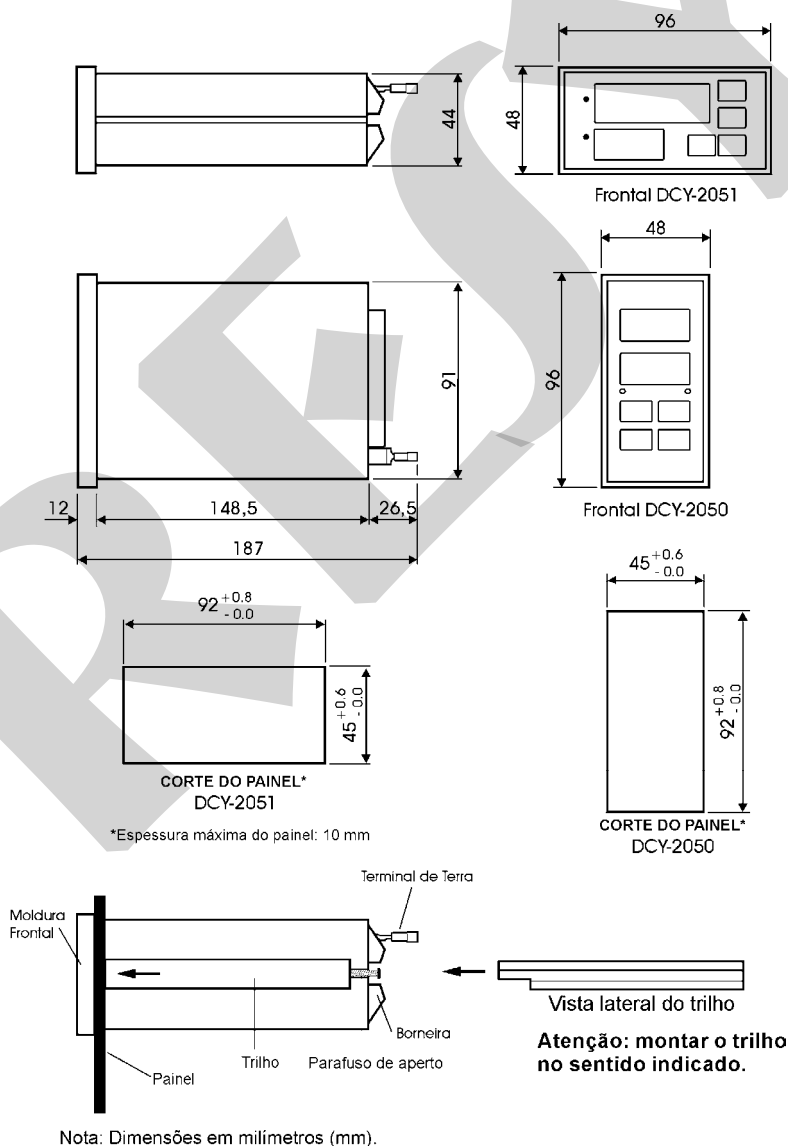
Desenho dimensional, corte e vista lateral da montagem no painel dos controladores DCY-2050/2051
